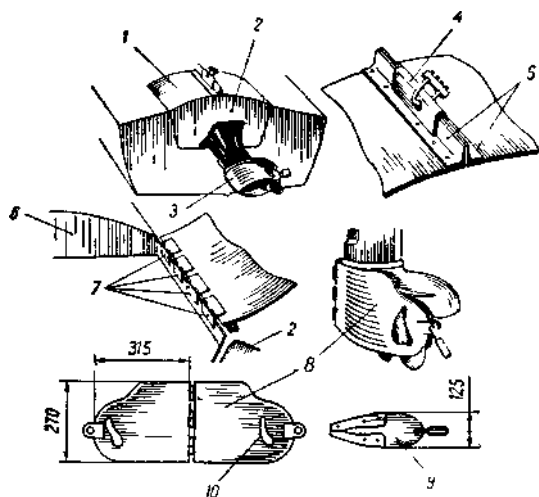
Приспособление для хранения мотора на лодке «Прогресс»
